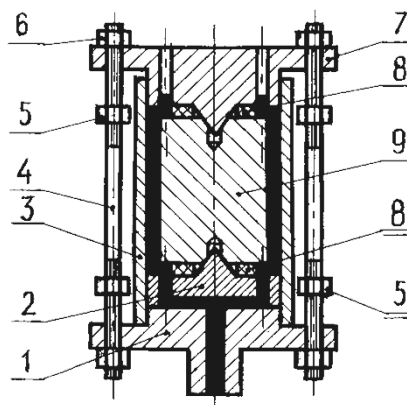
Схема приспособления для нанесения покрытия на образцы
